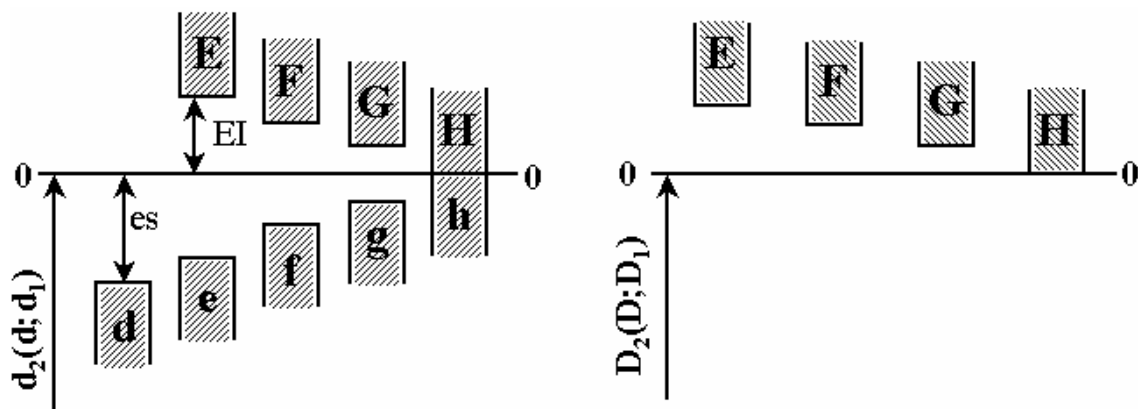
Схема расположения полей допусков резьбы
